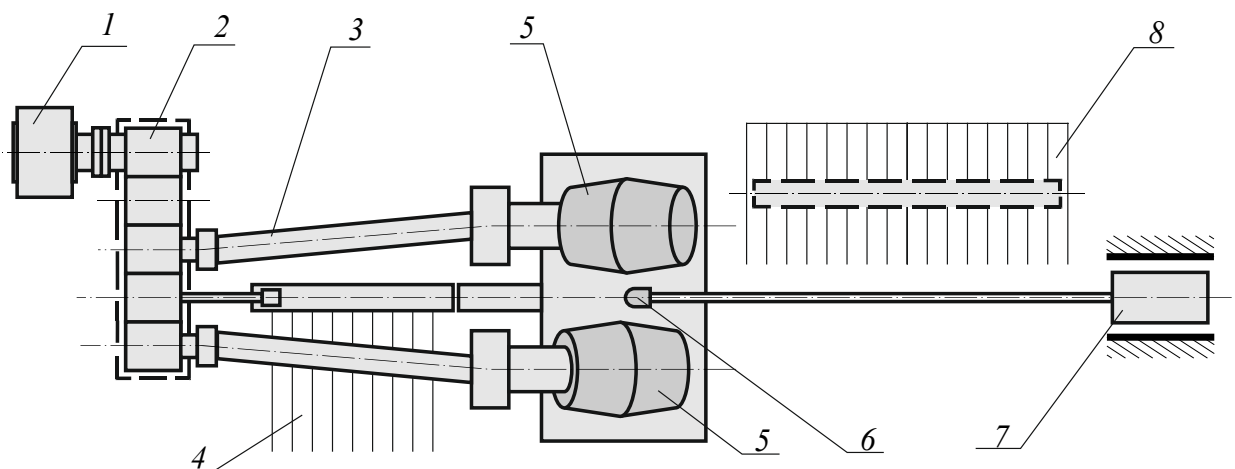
Принципиальная схема привода стана поперечно-винтовой прокатки: 1 – главный электродвигатель стана, 2 – комбинированный редуктор-шестеренная клетка, 3 – универсальные шпиндели, 4 – стол загрузки, 5 – прокатные валки, 6 – оправка, 7 – устройство для установки и перемещения оправки; 8 – наклонный стол
